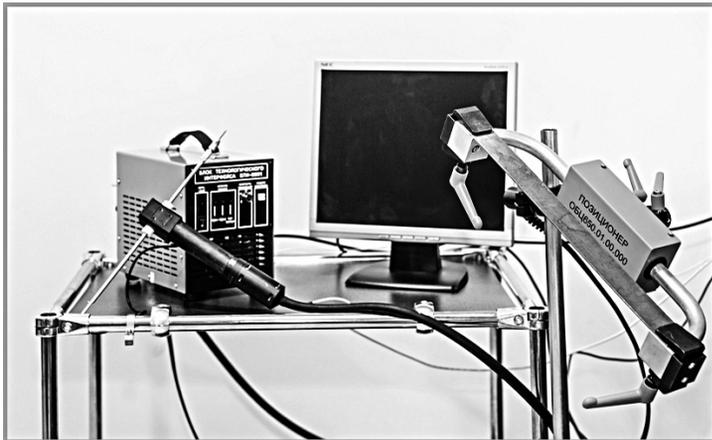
Общий вид малоамперного тренажера сварщика для электродуговой сварки МДТС-05 М1
